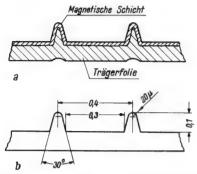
Vergrößerte Schnittzeichnung der Tonträgerplatte; erplatte; a = Trägerfolie mit aufgegossener Schicht, b = Rillenprofil (Maße in Millimeter)
